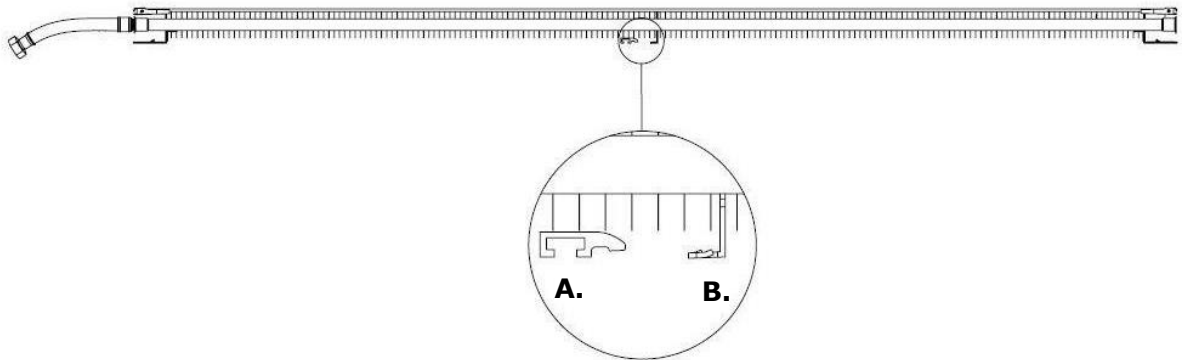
verstevigingsplaat voor Oost-West opstellingen (Sunbeam Symmetrical)
